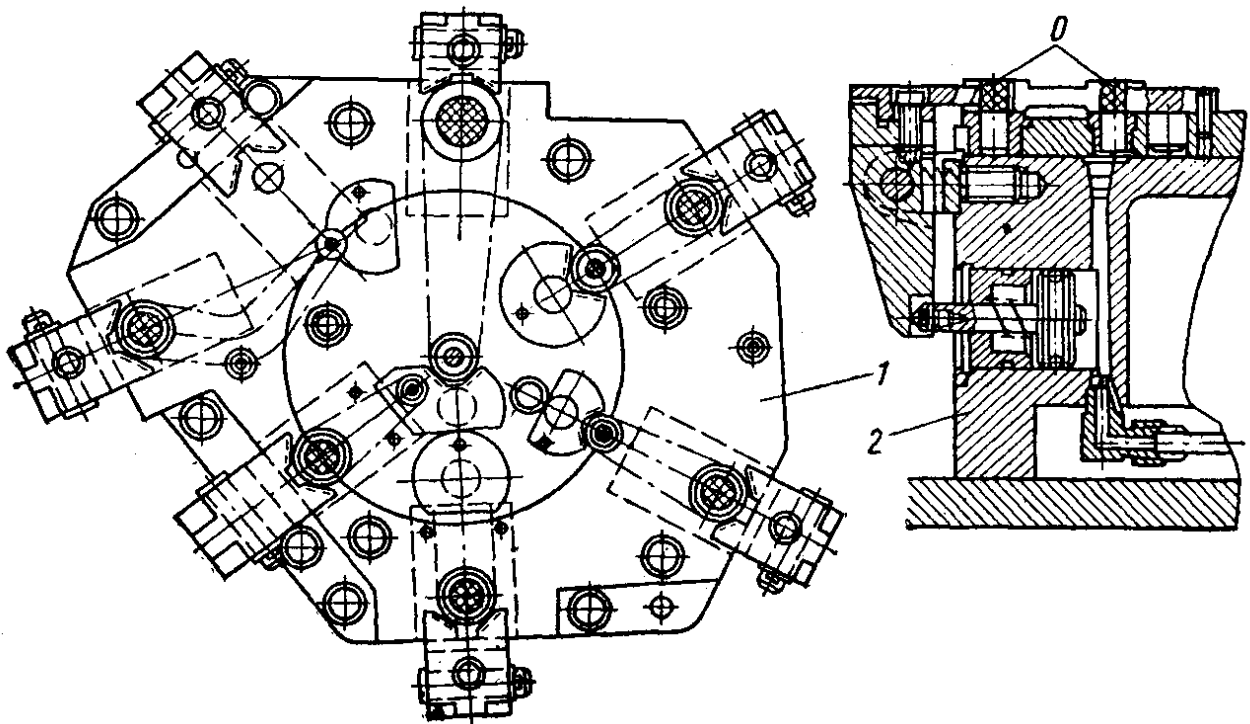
Схема встановлення важелів на агрегатному багатошпindelьному чотирьох позиційному свердильному верстаті
